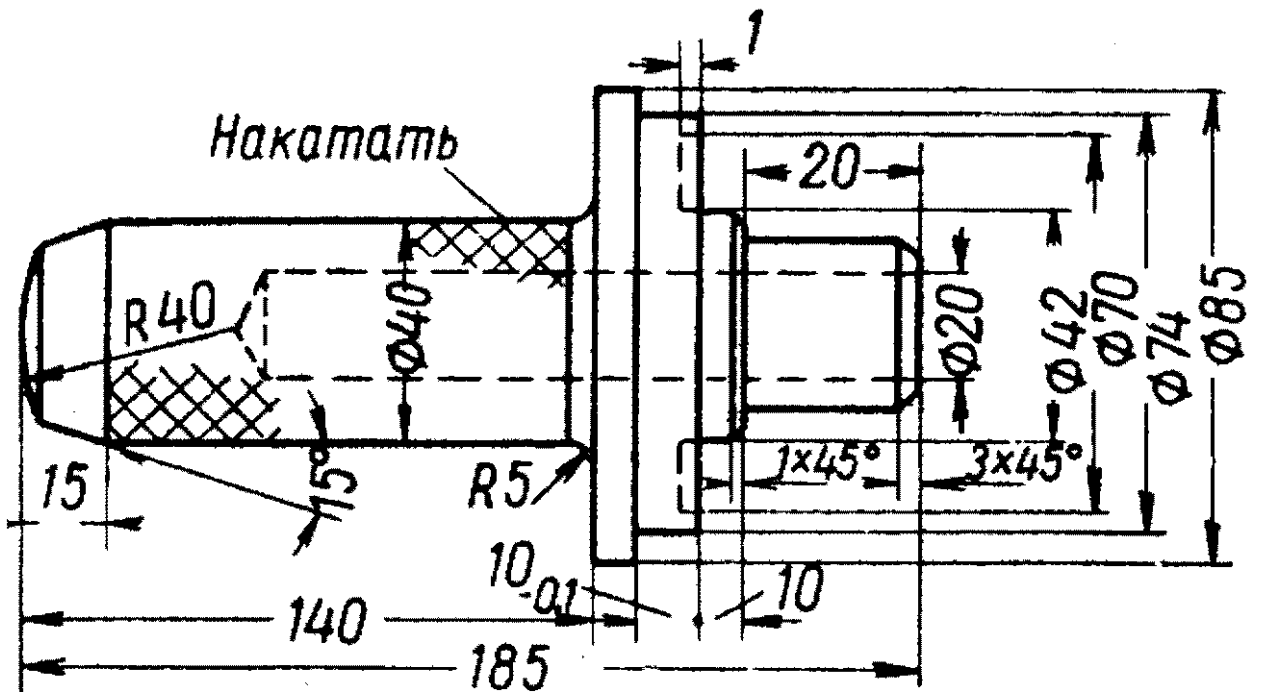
Оправка для запрессовки внутреннего сальника вала ведущей шестерни
